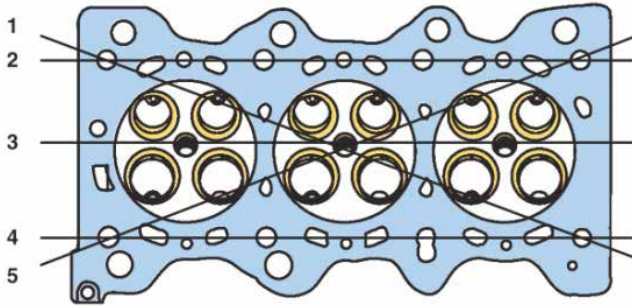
Сопрягаемая с прокладкой поверхность головки цилиндров должна быть проверена в пяти направлениях на коробление; искривление; изгиб и скручивание; источник: *Pearson Education, Inc.
